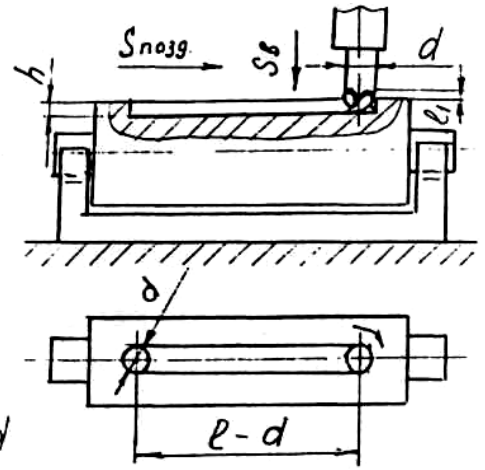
Схема фрезерування канавки закритої з двох боків
